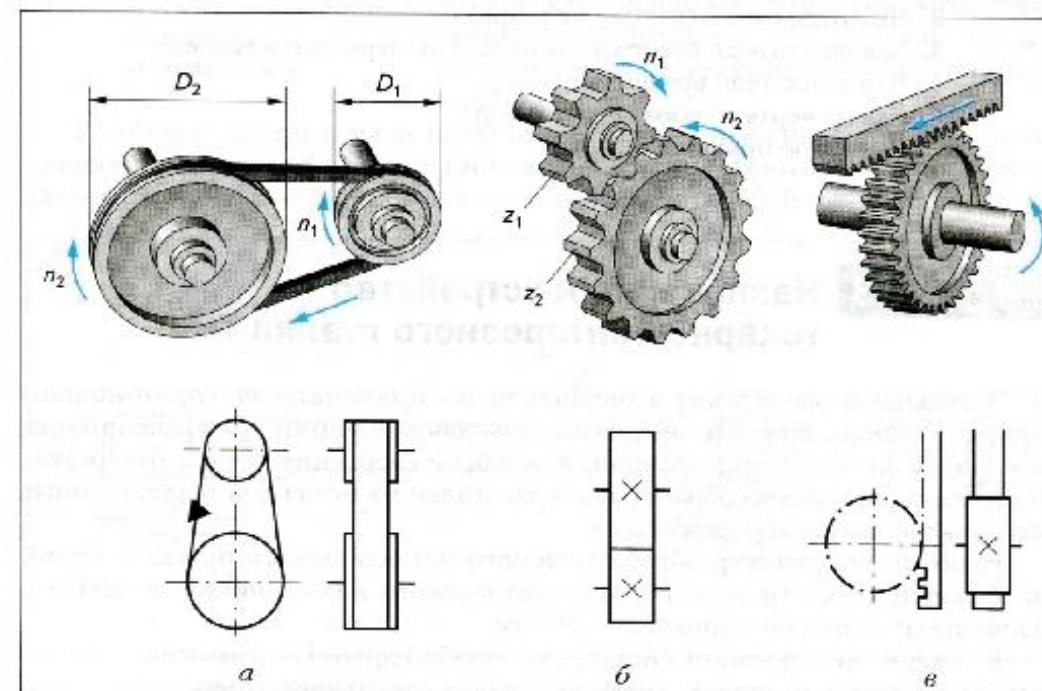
Виды механических передач, применяемых в токарном станке, и их условные обозначения: а — ремённая; б — зубчатая; в — реечная
